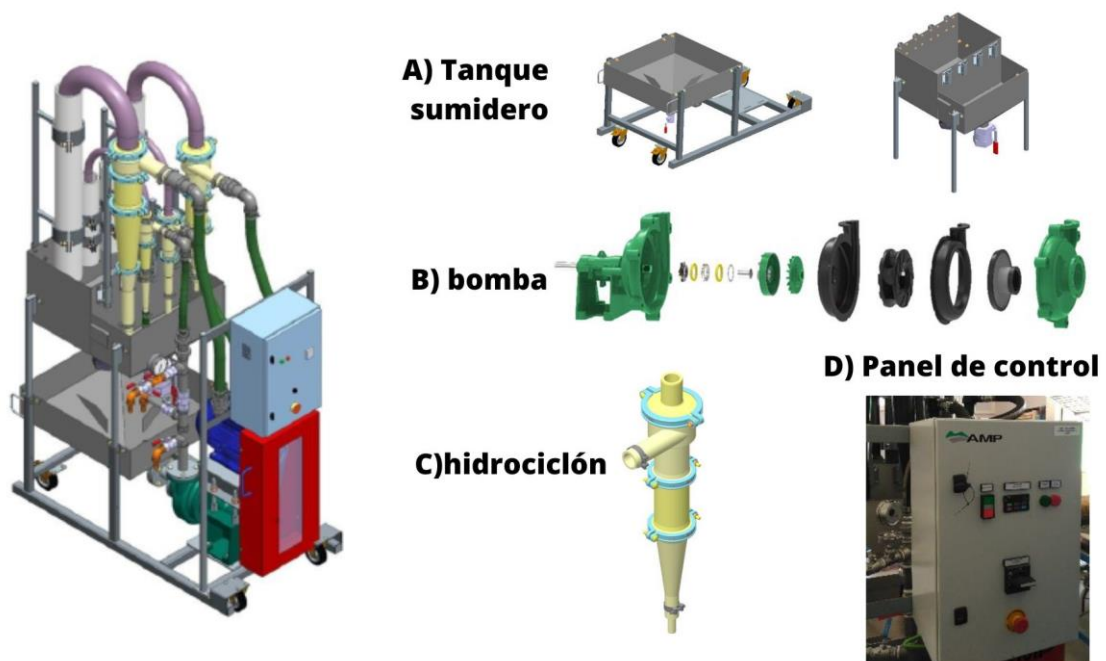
Partes de la planta piloto a escala laboratorio (Fuente: AMP)
